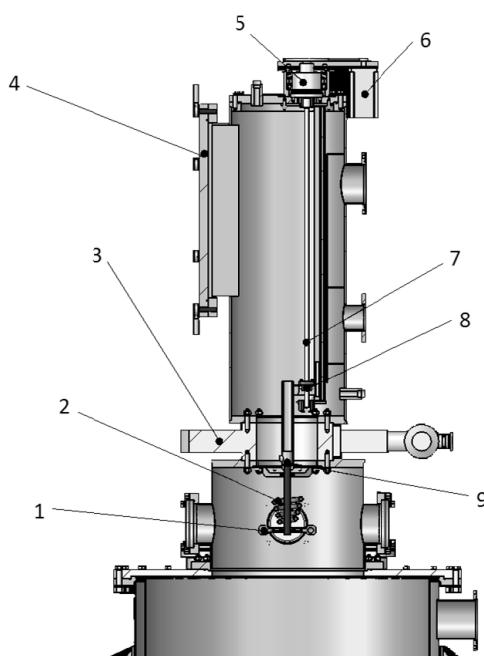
Схема подачи заготовки УРМ-002: 1 – распылительная форсунка; 2 – индуктор; 3 – вакуумный затвор; 4 – загрузочный люк; 5 – магнитная муфта; 6 – электрический двигатель; 7 – винт; 8 – каретка; 9 – заготовка
